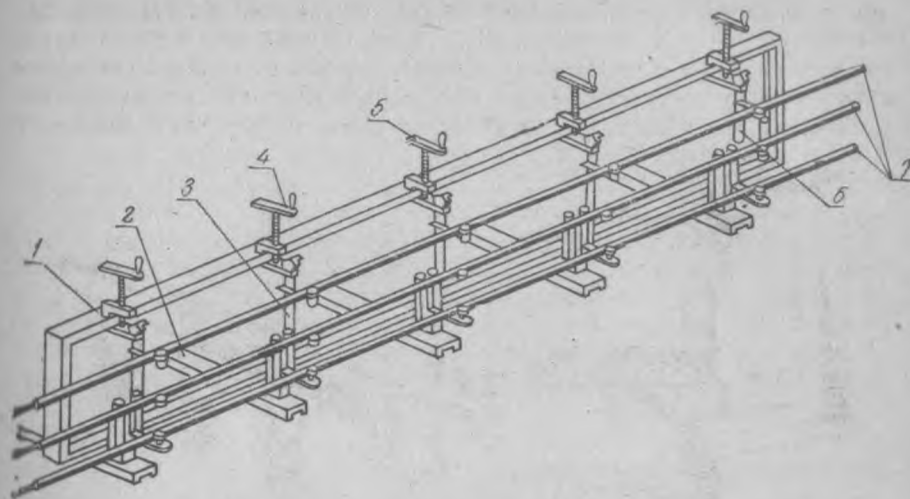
Кондуктор для сборки троллеев в блоки
